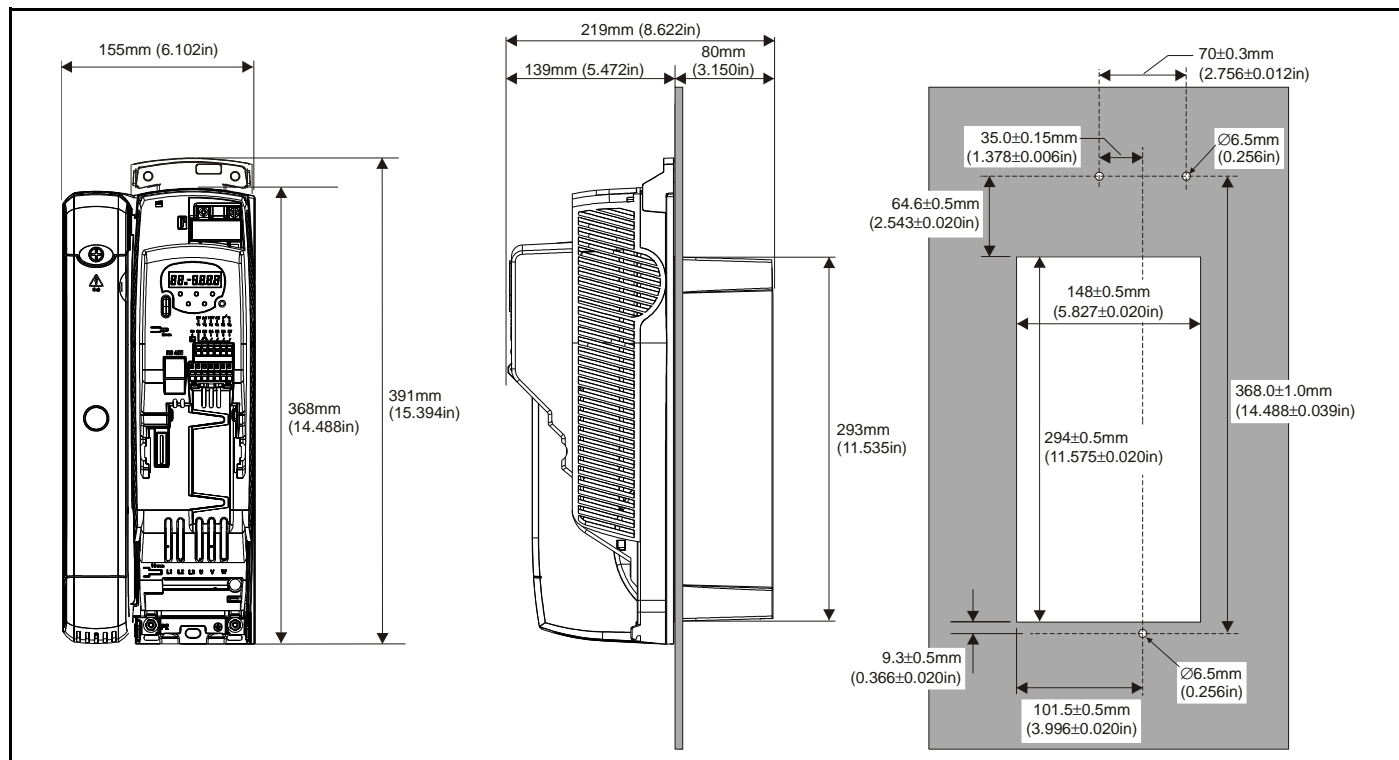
Montaż powierzchniowy Commander SK Rozmiar 6
